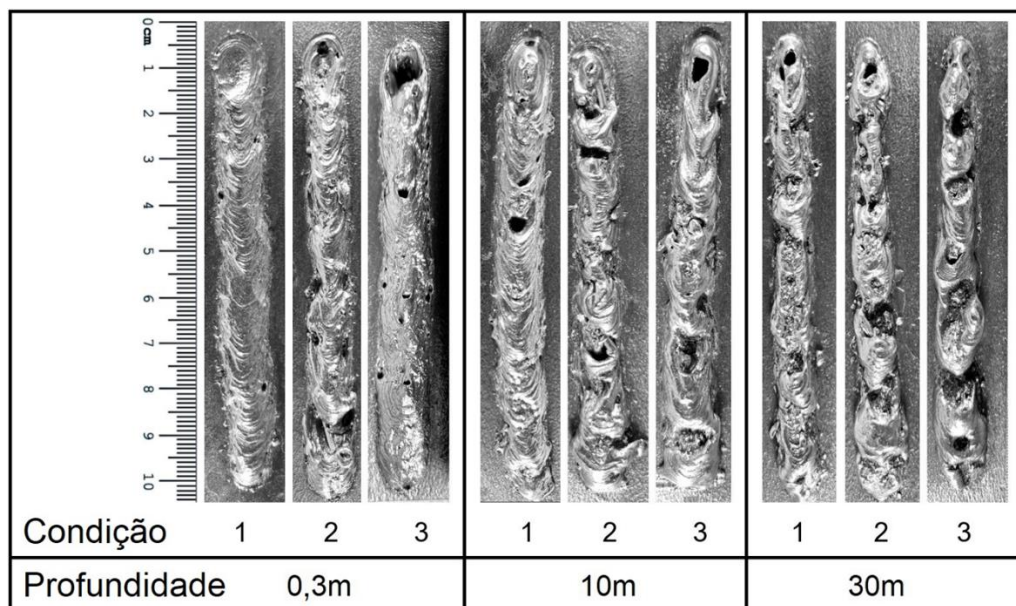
Imagens dos cordões de solda produzidos em cada condição.
